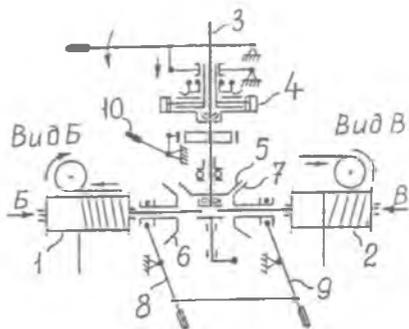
Схема силовой передачи ветряка с приводом на барабаны для тросовой тяги
